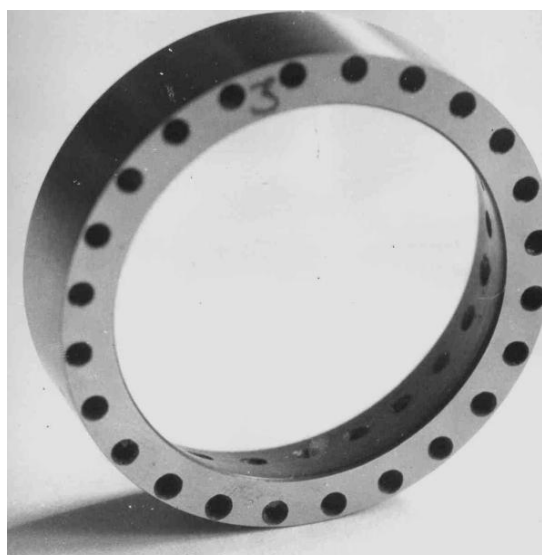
Внешний вид неподвижного образца с отверстиями для крепления термопары
